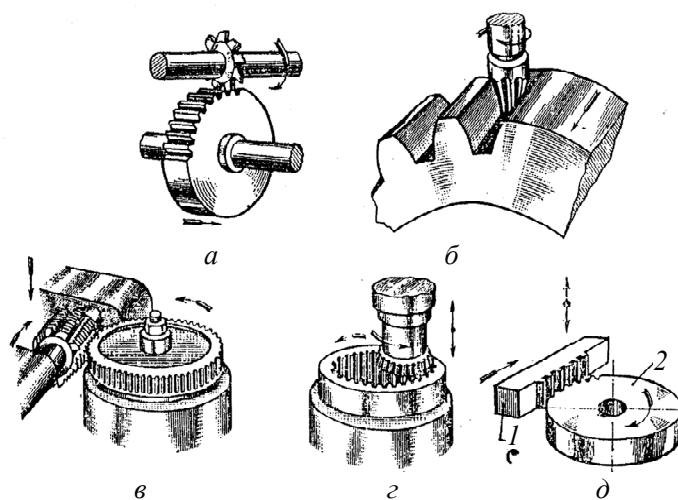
Методи виготовлення зубчастих коліс:
